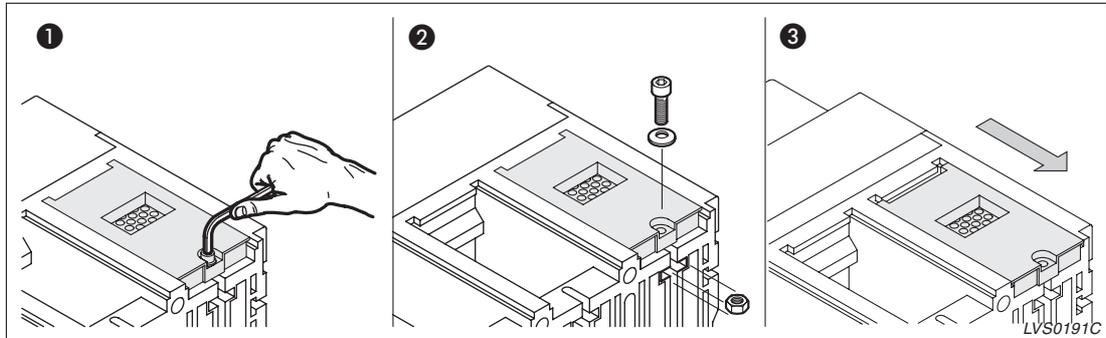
Lösen der Innensechskantschraube der Lichtbogenlöschkammer
